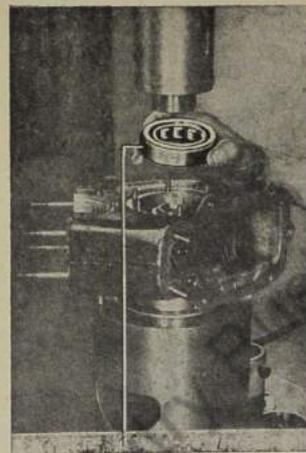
Zylinderrollenlager in Zwischenradgehäuse einpressen
